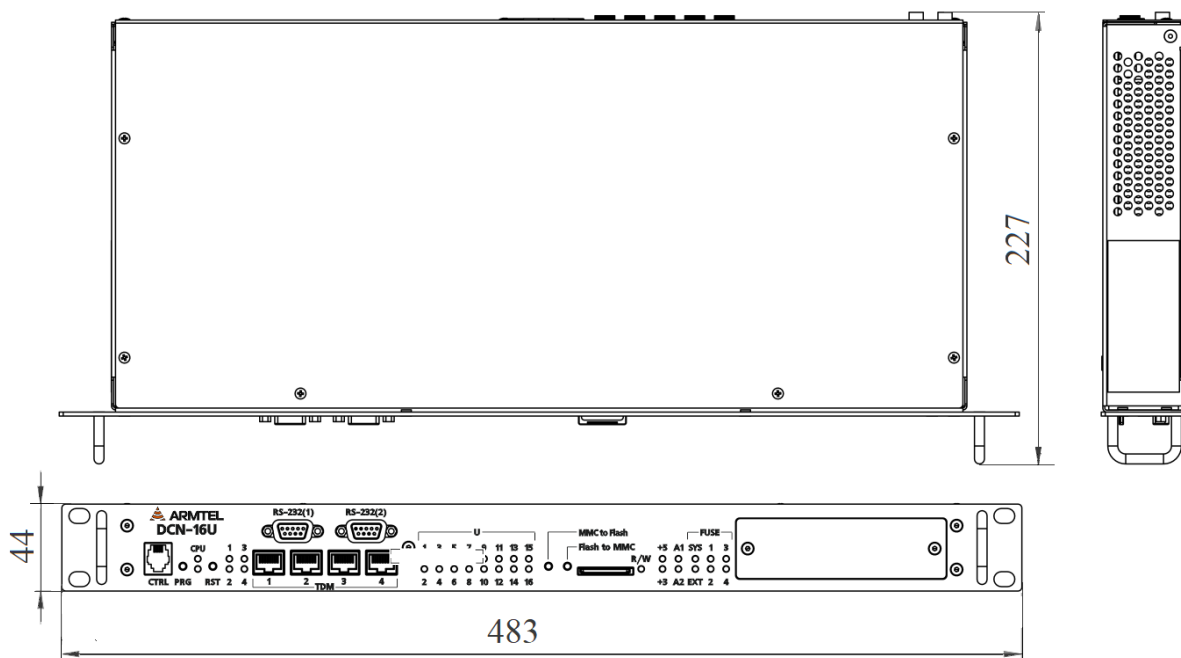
Внешний вид и габаритные размеры DCN-16U
